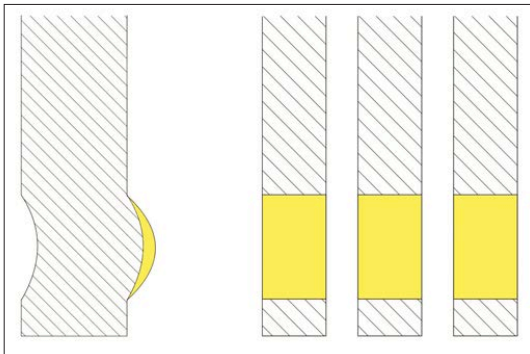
Ergebnis der Beschichtung mit Brushtechnik [2]
